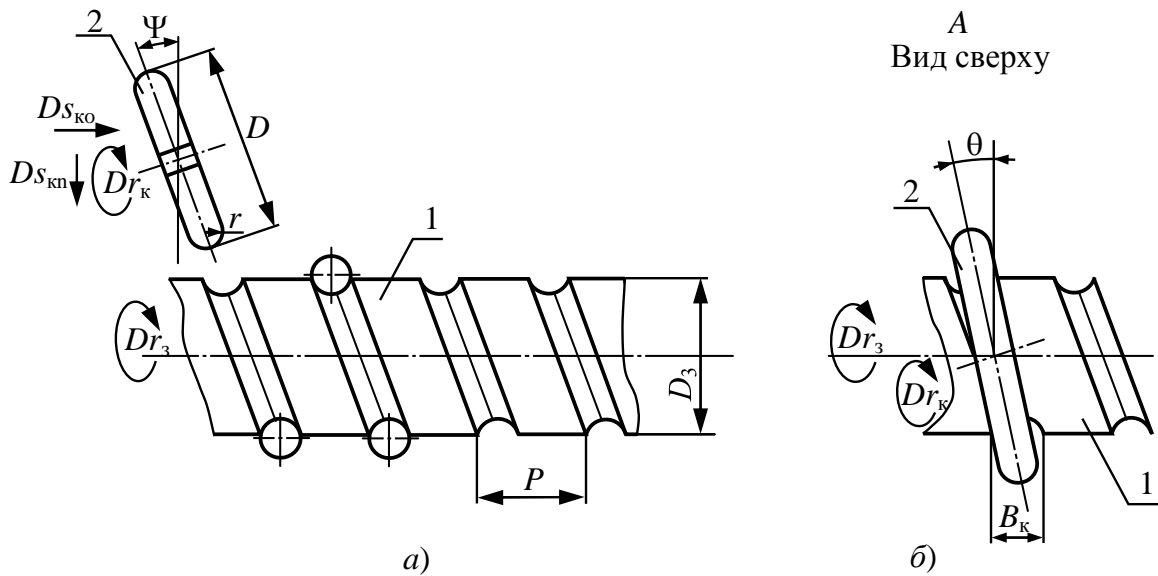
Схема шлифования наружных винтовых канавок за счёт дополнительного поворота круга: *а* – вид спереди; *б* – вид сверху
